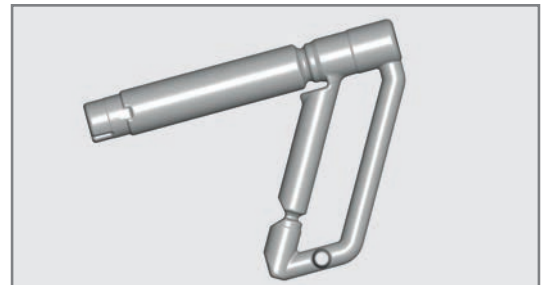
CAD-Modell des additiv gefertigten Kernes für ein Wasserhahnus-teil aus Messing. Druckmaterial für den Kern: Quarzsand mit Furanharzbinder
